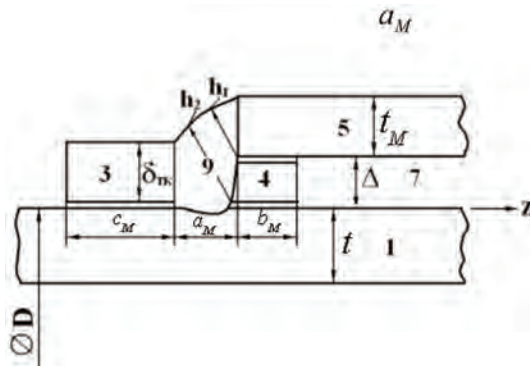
Схема перерізу кільцевого з'єднання монтажного вузла кріплення герметичної муфти з компаундним наповнювачем до трубопроводу [5.1]
